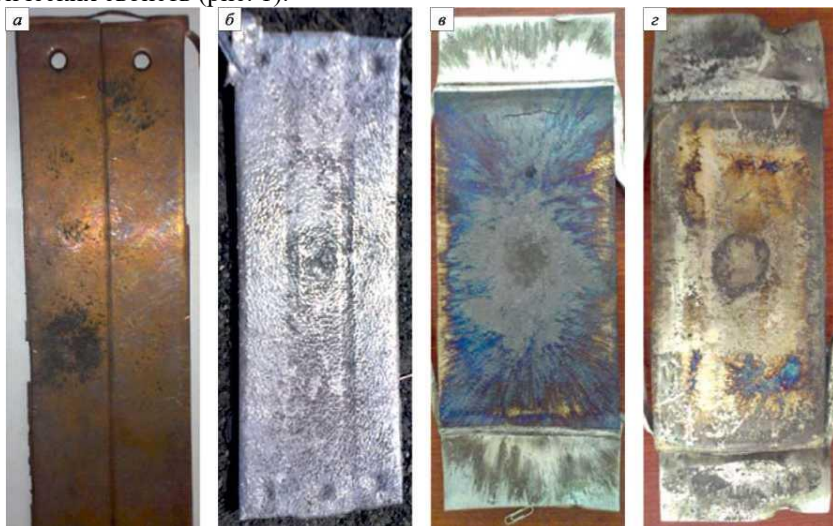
Композиции, полученные сваркой взрывом:
